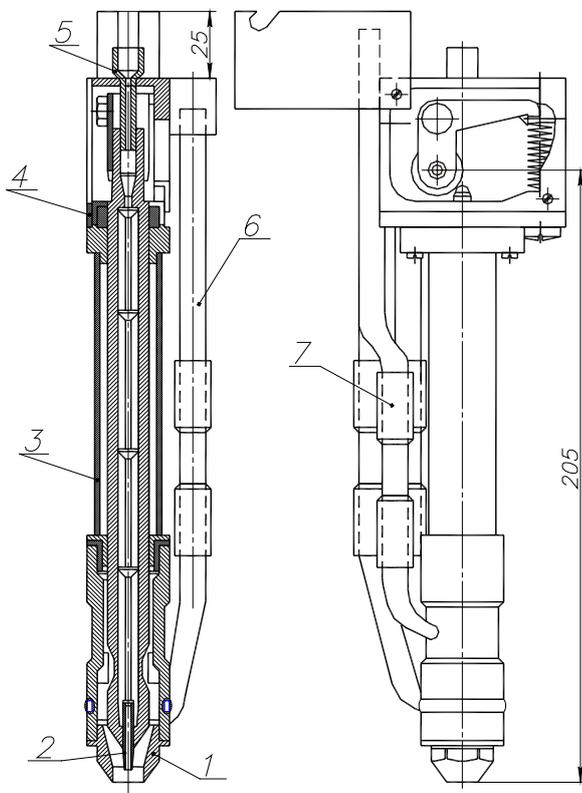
Сварочная головка для автоматизированной сварки плавящимся электродом (проволокой). 1 – сопло, 2 – сменный наконечник; 3 – горелка; 4 – корпус плазмотрона; 5 – направляющая втулка; 6 – трубка подвода охлаждения; 7 – подвод защитного газа
